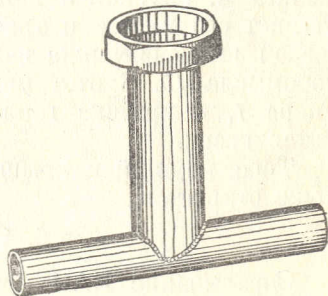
Ключ для отвертывания пробки заливной горловины.
